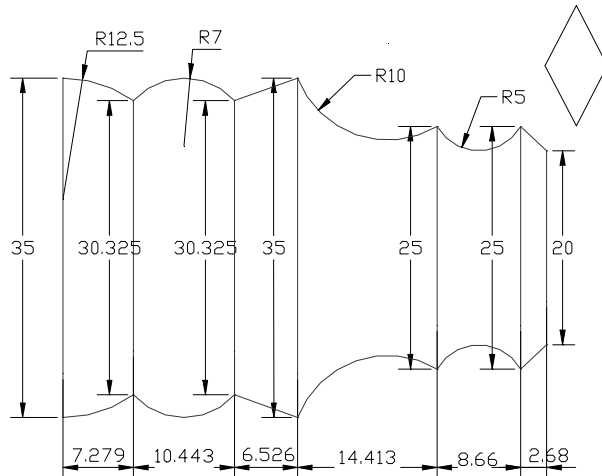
Peça 1, perfil a ser usinado e posição da ferramenta (Cotas em mm).
